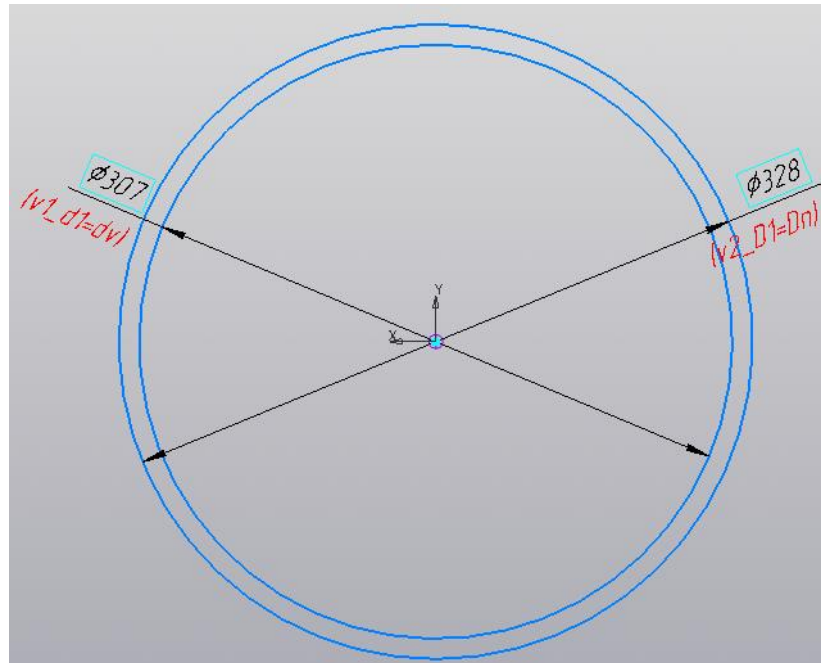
Типовой эскиз для класса изделий типа «Кольцо»
